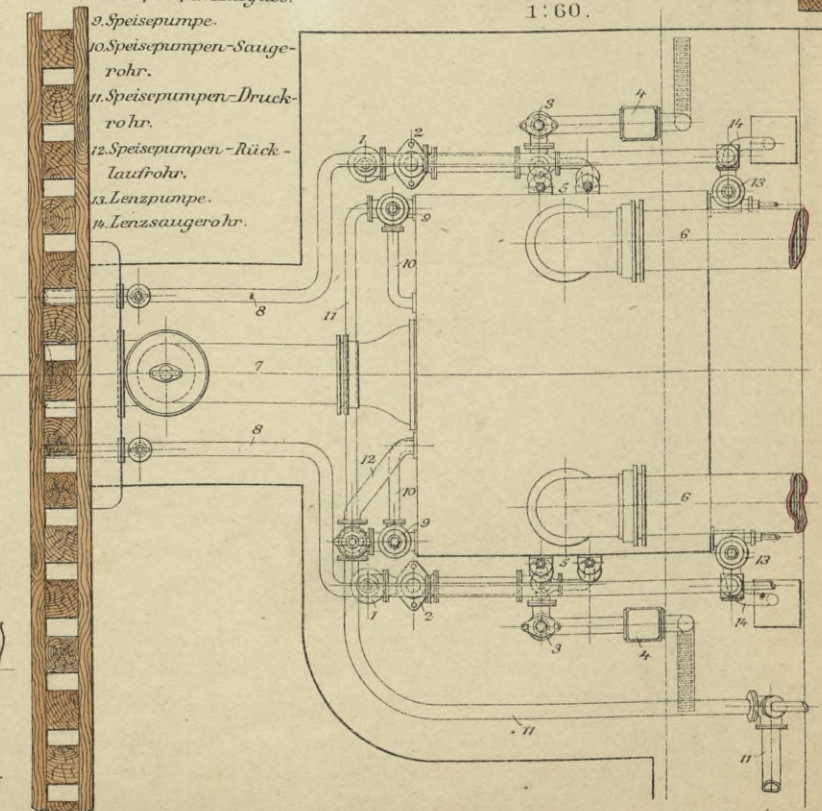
Grundriss des Condensator-Arrangements.
